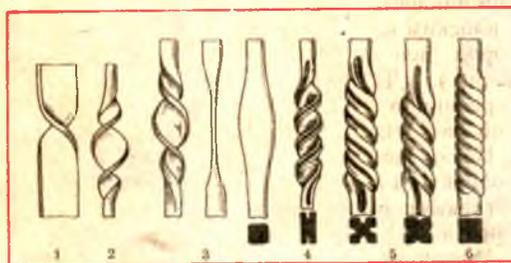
Типы скруток из: 1 — плоской заготовки; 2 — раскованной круглой заготовки; 3 — раскованной квадратной заготовки; 4 — плоской заготовки с «дорожкой»; 5 — квадратной заготовки с двумя «дорожками»; 6 — квадратной заготовки
